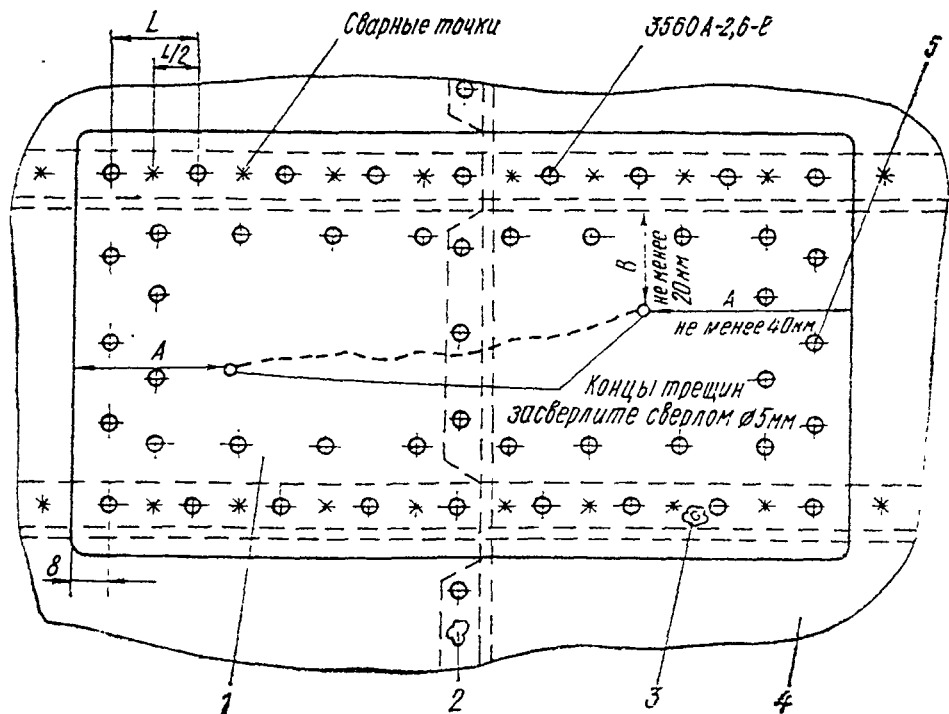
Типовой ремонт обшивки gondoly двигателя при расположении трещин вблизи силовых элементов:
